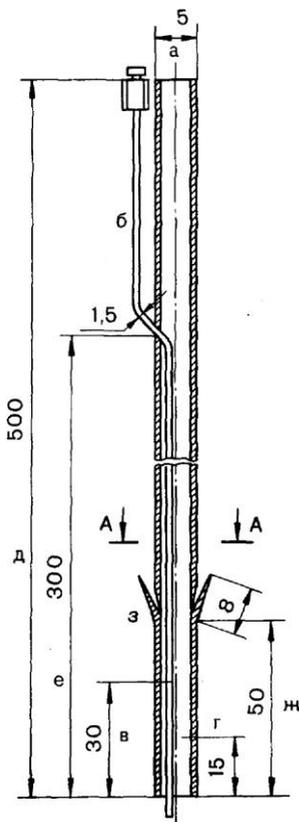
Схема-чертеж трубки для введения в желчный пузырь после лапароскопической пункции его [Жидовинов Г. И., Корсаков А. В., 1986]. Цифры означают размеры в миллиметрах.
